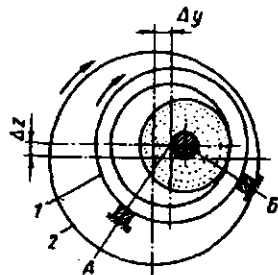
Схема внутреннего шлифования на жестких опорах: 1 – обрабатываемая деталь; 2 – ведущая планшайба; Δz и Δy – смещение оси обрабатываемой детали относительно оси планшайбы
